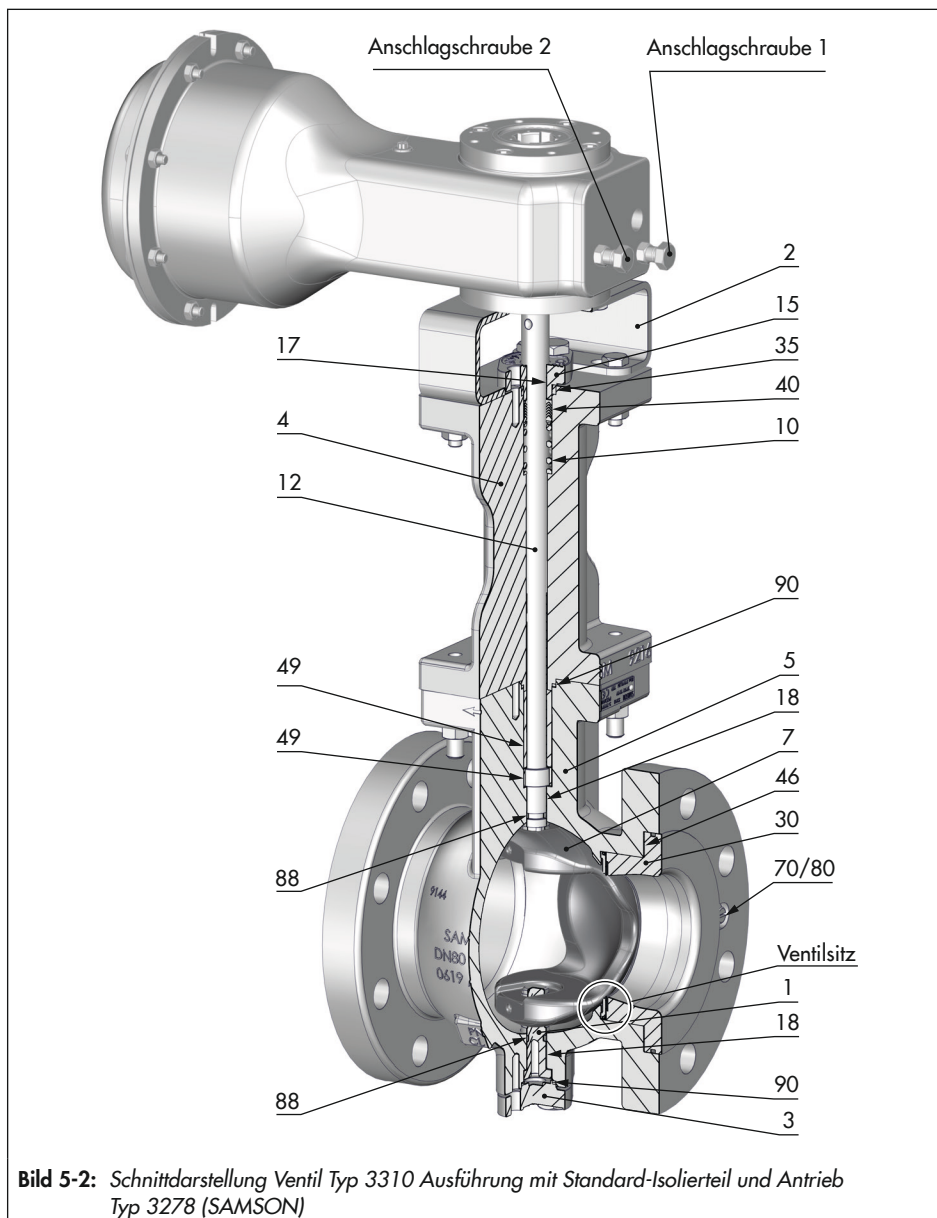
Schnittdarstellung Ventil Typ 3310 Ausführung mit Standard-Isolierteil und Antrieb Typ 3278 (SAMSON)
